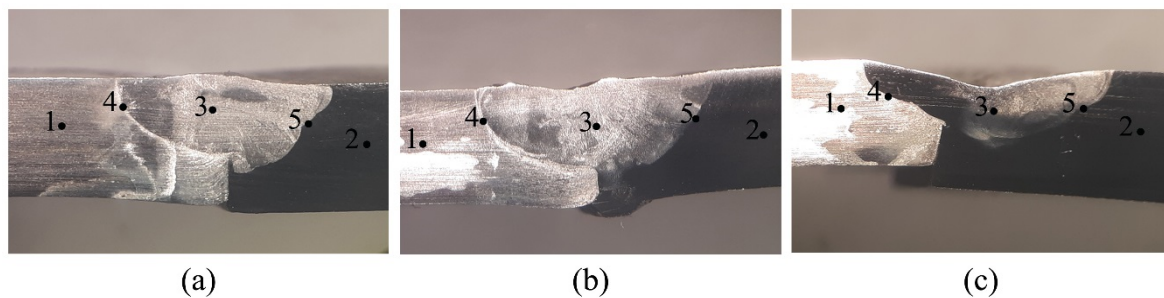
Imagem das amostras soldadas 0-33 (a), 0-40 (b) e 0-50 (c) e a indicação das diferentes regiões analisadas eletroquimicamente: 1) 316L; 2) Inconel 718; 3) Zona fundida (ZF); 4) região entre 316L e ZF; 5) região entre Inconel e ZF.
